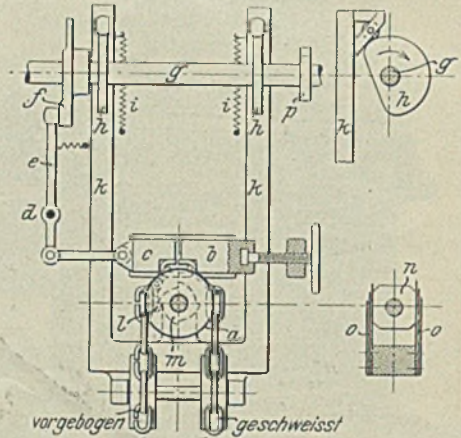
Schema der Kettenschweißmaschine.
